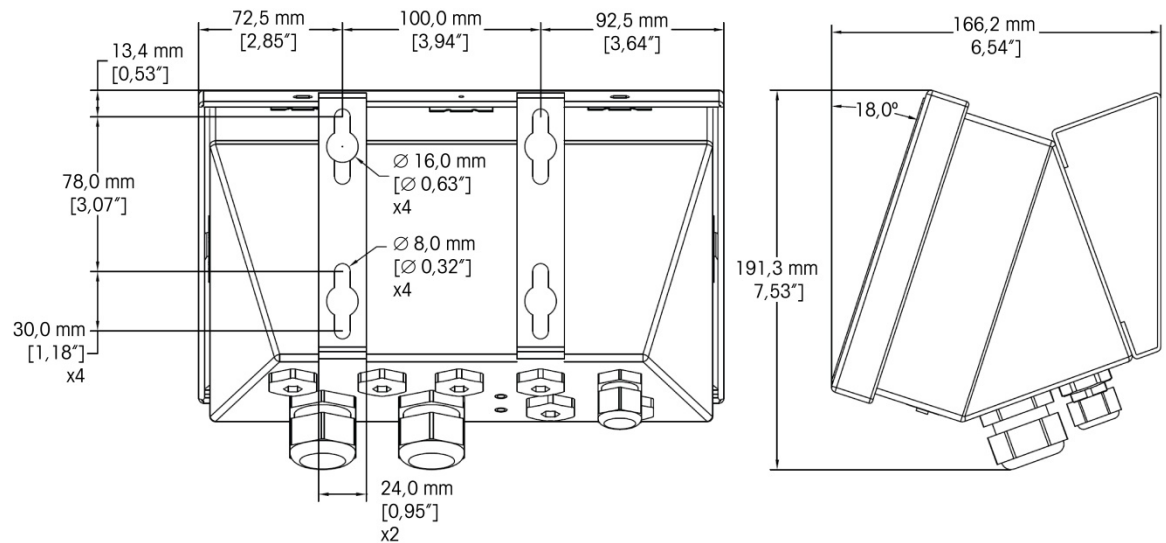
Dimensiones de la caja para ambientes adversos del IND570 con soportes de montaje de ángulo fijo, montaje VESA
